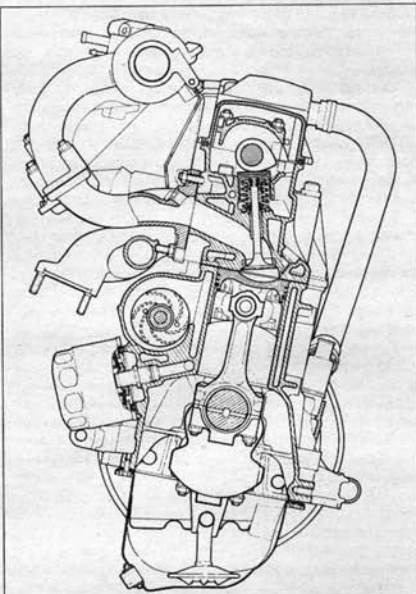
Поперечный разрез двигателя ВА3-2111
